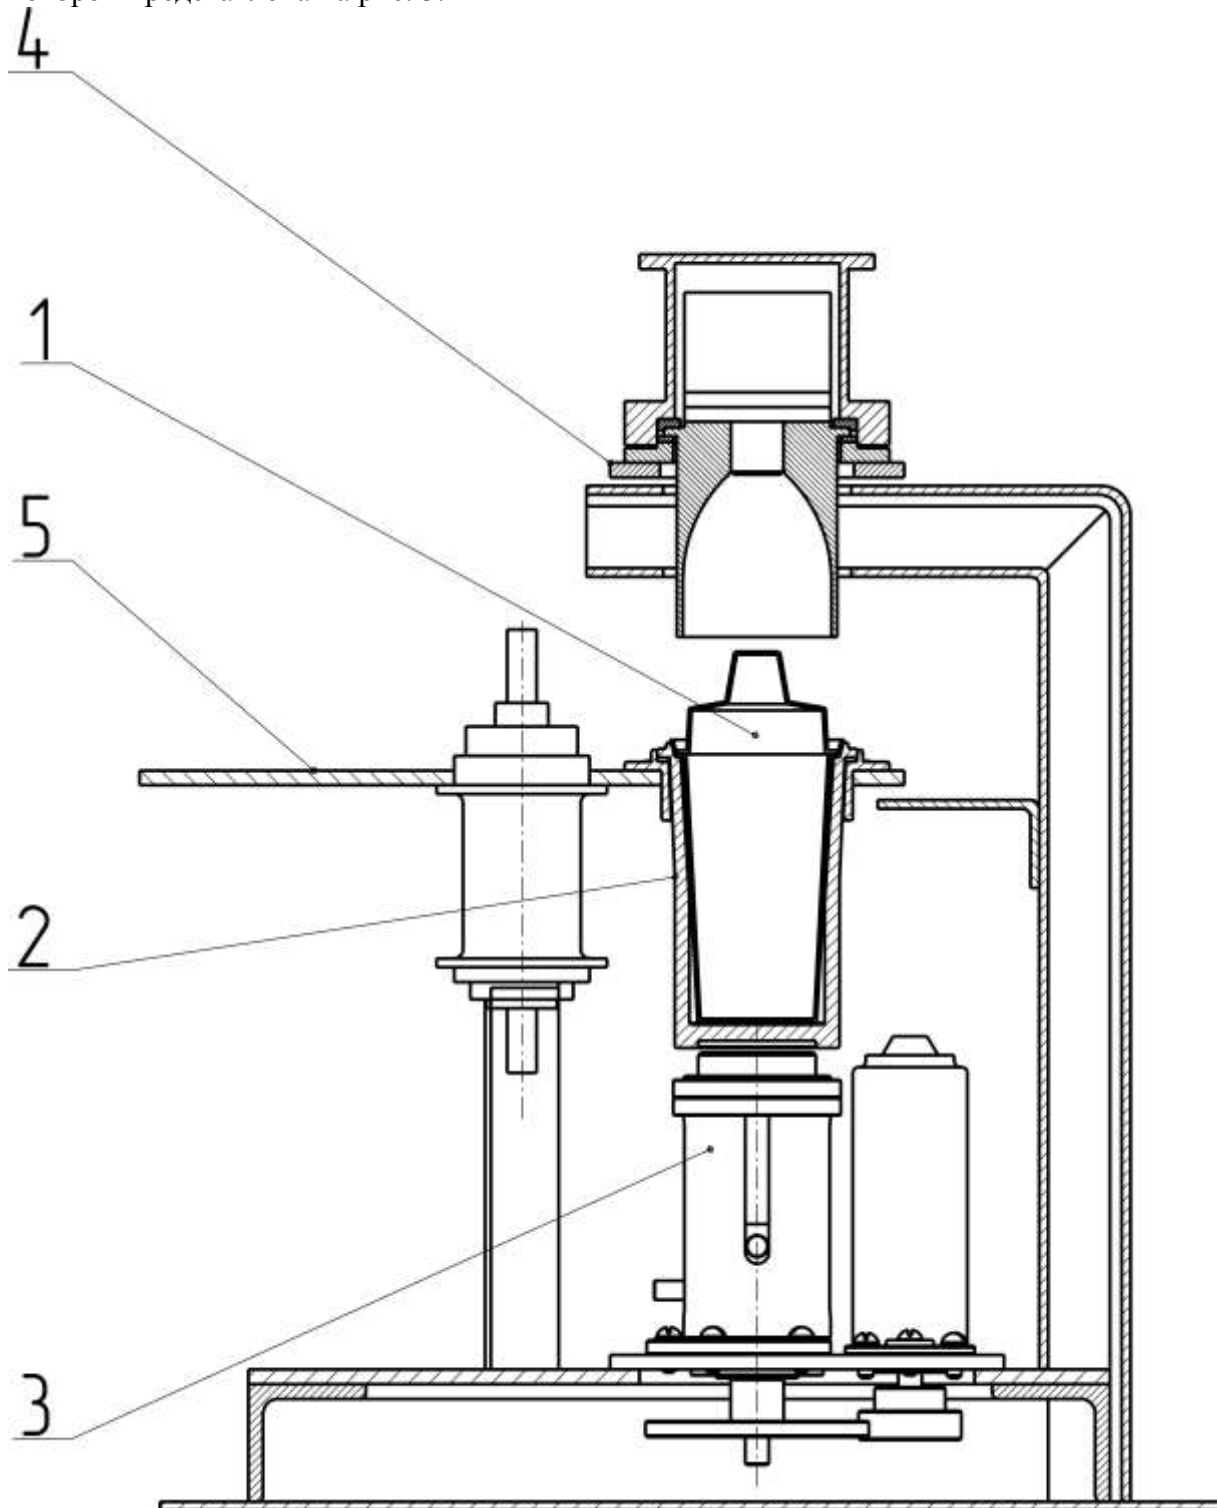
Установка для сварки элементов картриджа.
